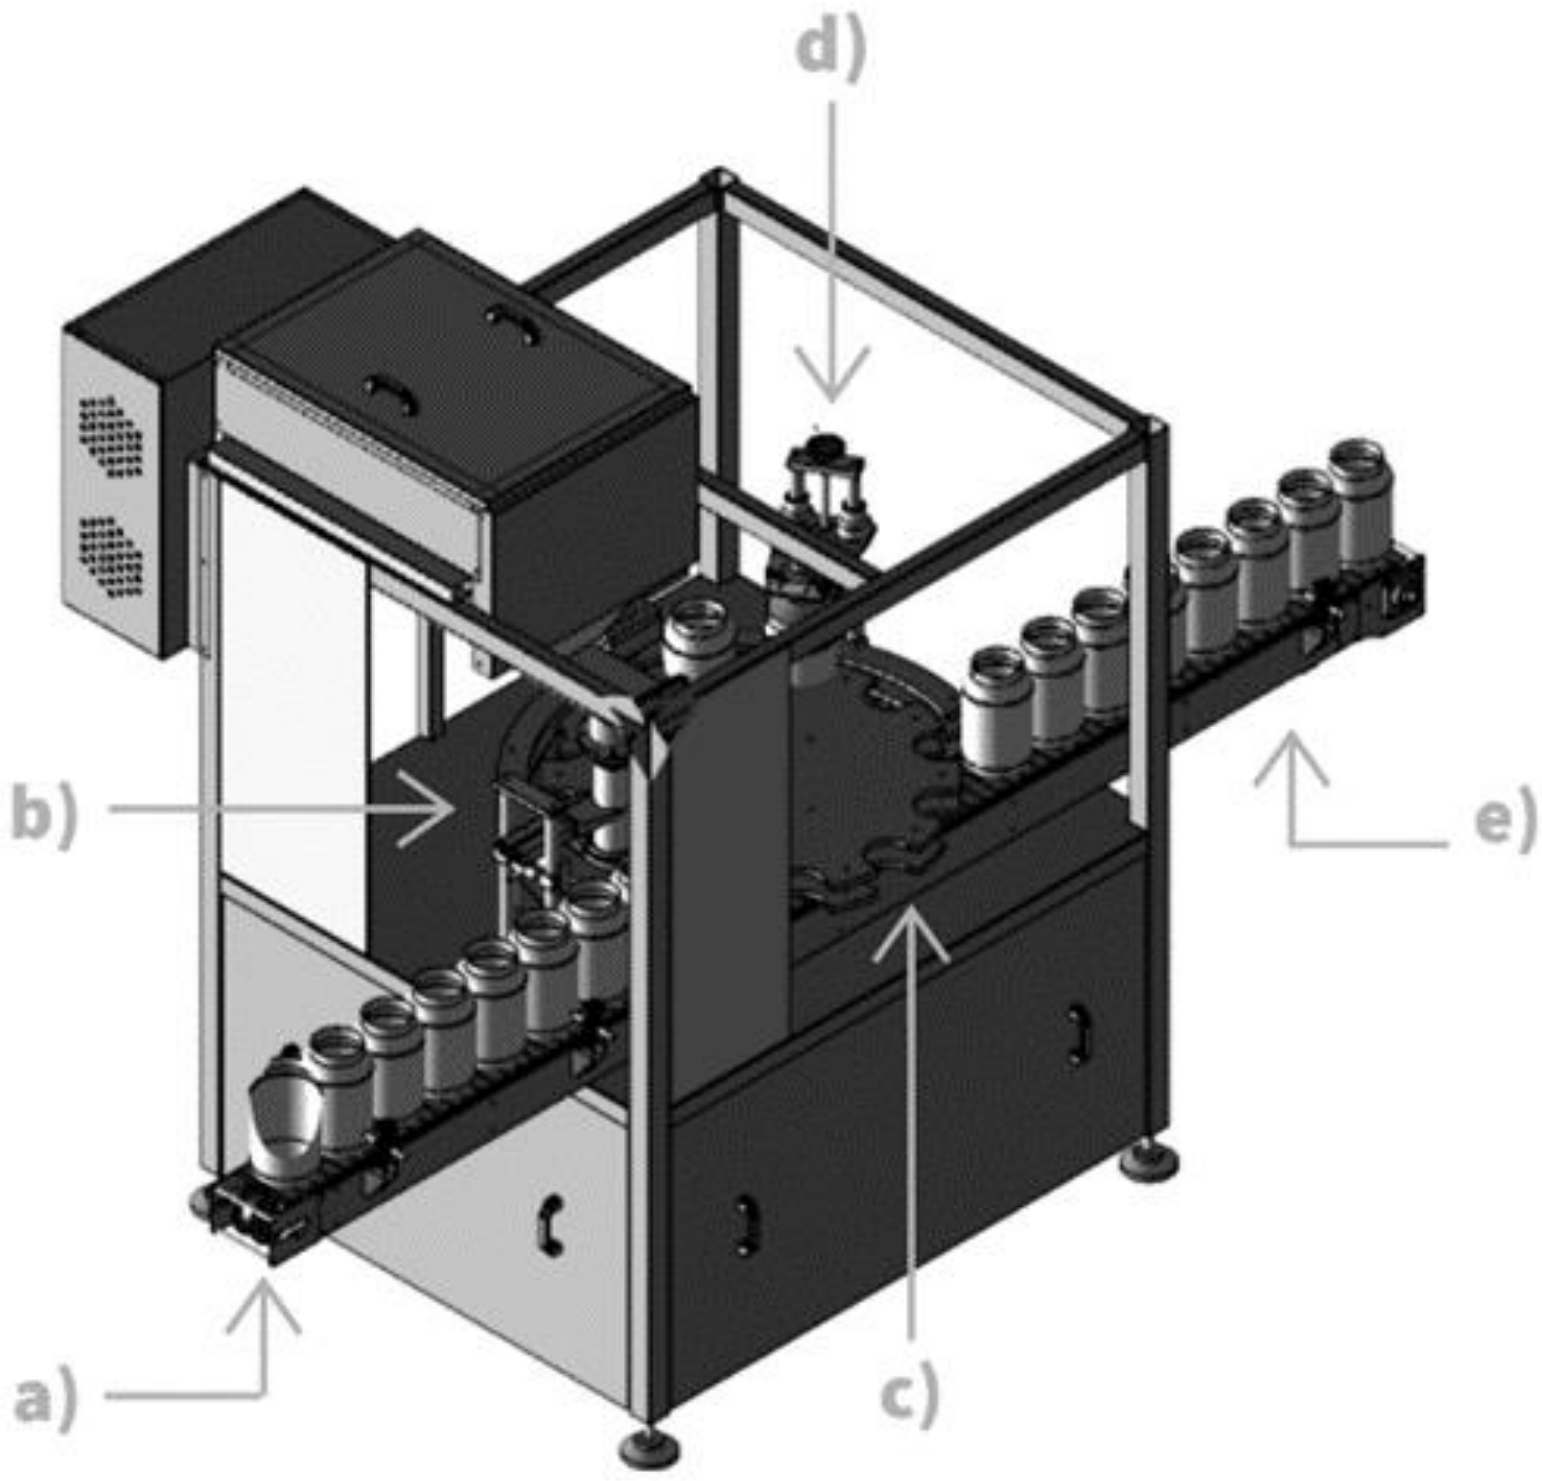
Diseño conceptual inicial. (a) transporte inicial, (b) dispensador, (c) posicionador, (d) sellado y (e) transporte final.
